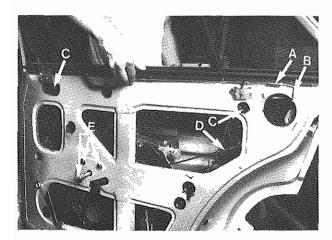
A - Registro tirante Rod adjuster B - Tirante rinvio "sicura"
